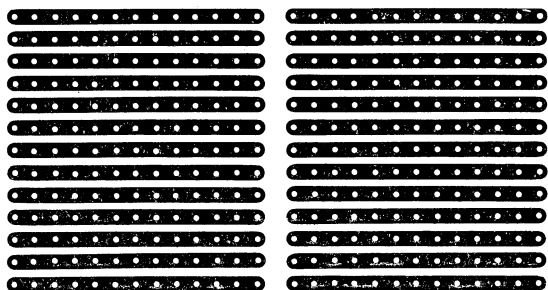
Universalleiterplatte mit 5-mm-Raster
